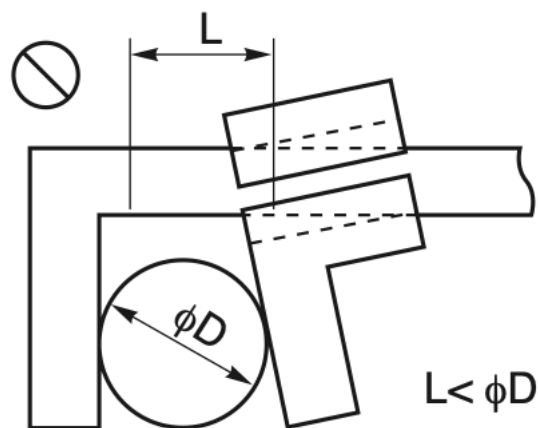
Možnosti měření s posuvným měřítkem [12]
